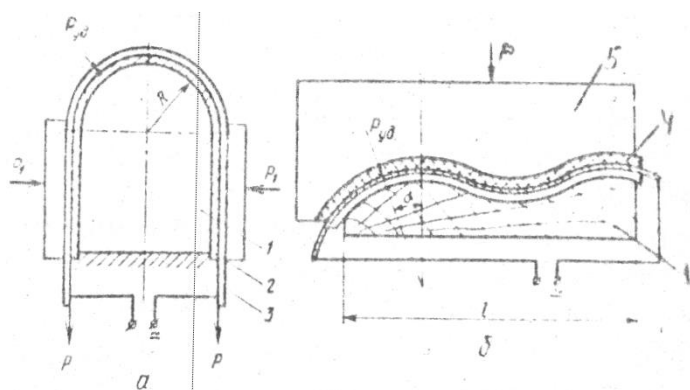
Схеми пристроїв для облицювання криволінійних поверхонь: а - гнучкою стрічкою; б - контршаблоном: 1 - облицювана деталь; 2 - шпон; 3 - гнучка стрічка; 4 - компенсуюча прокладка; 5 - контр шаблон.
